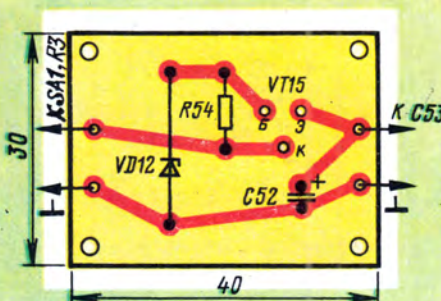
Печатная плата стабилизатора напряжения +5 В
